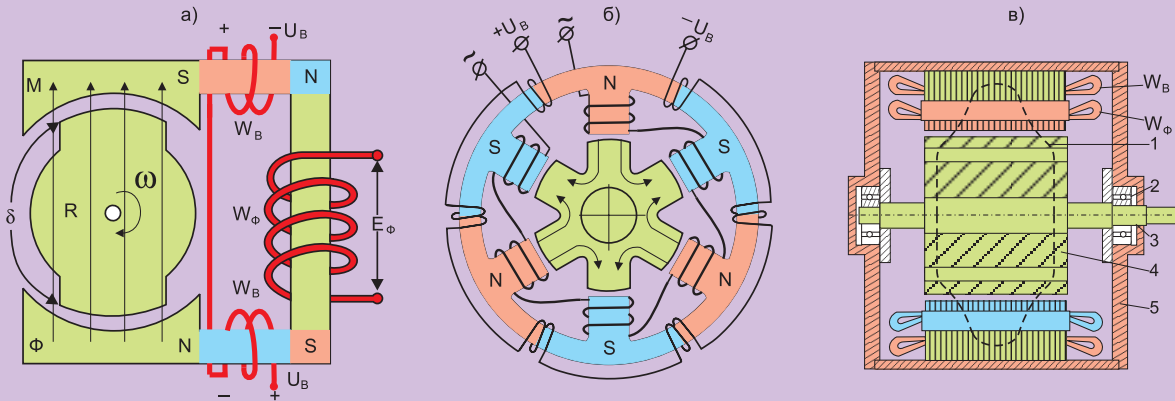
Индукторный генератор переменного тока с расположением обмоток  $W_B$  электромагнитного возбуждения на статоре: а — модель генератора; б — схема соединения обмоток на однофазном статоре; в — упрощенная конструкция генератора; 1 — паз ротора; 2 — подшипник; 3 — вал ротора; 4 — полюс ротора; 5 — корпус генератора;  $W_B, W_Ф$  — обмотки возбуждения и фазные.
